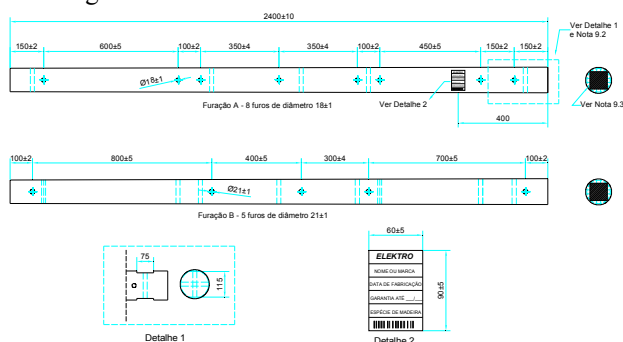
Cruzeta roliça resinada 2.400 mm – Dimensões em Milímetros.
